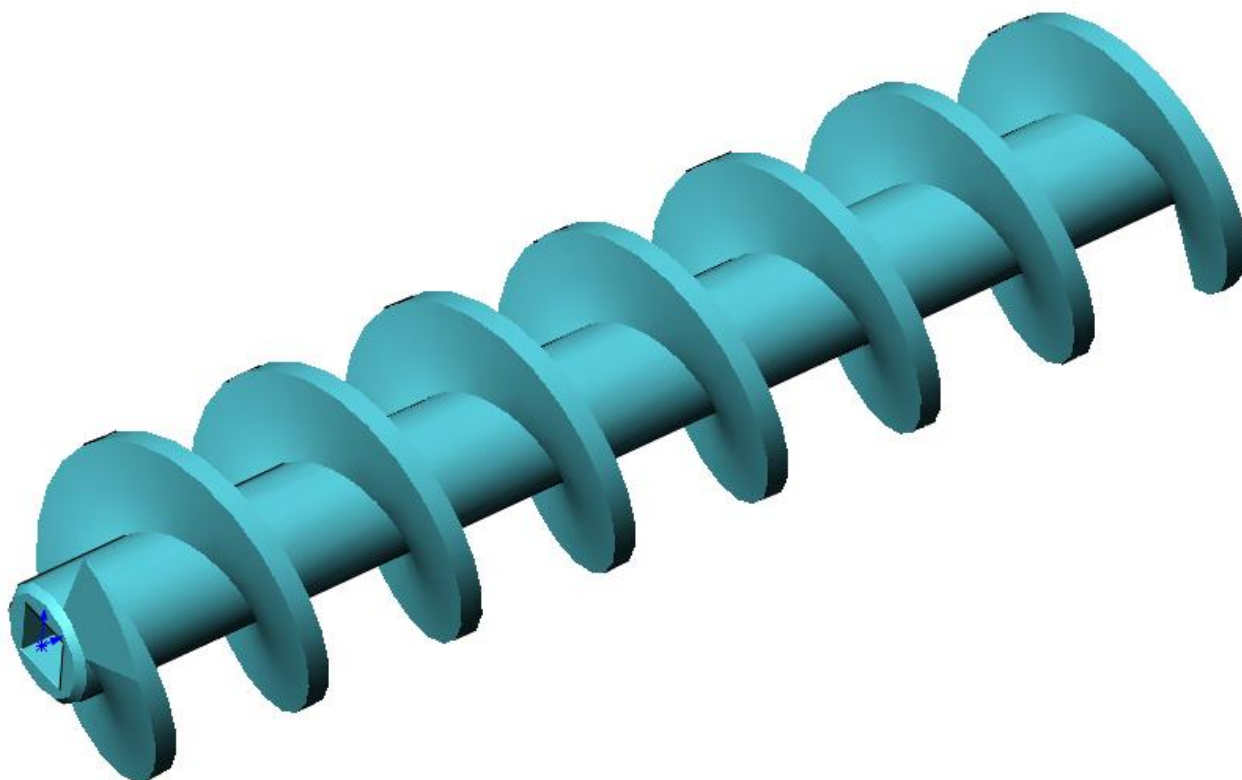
Конструктивна схема шнека вузла нагнітання фаршу.
